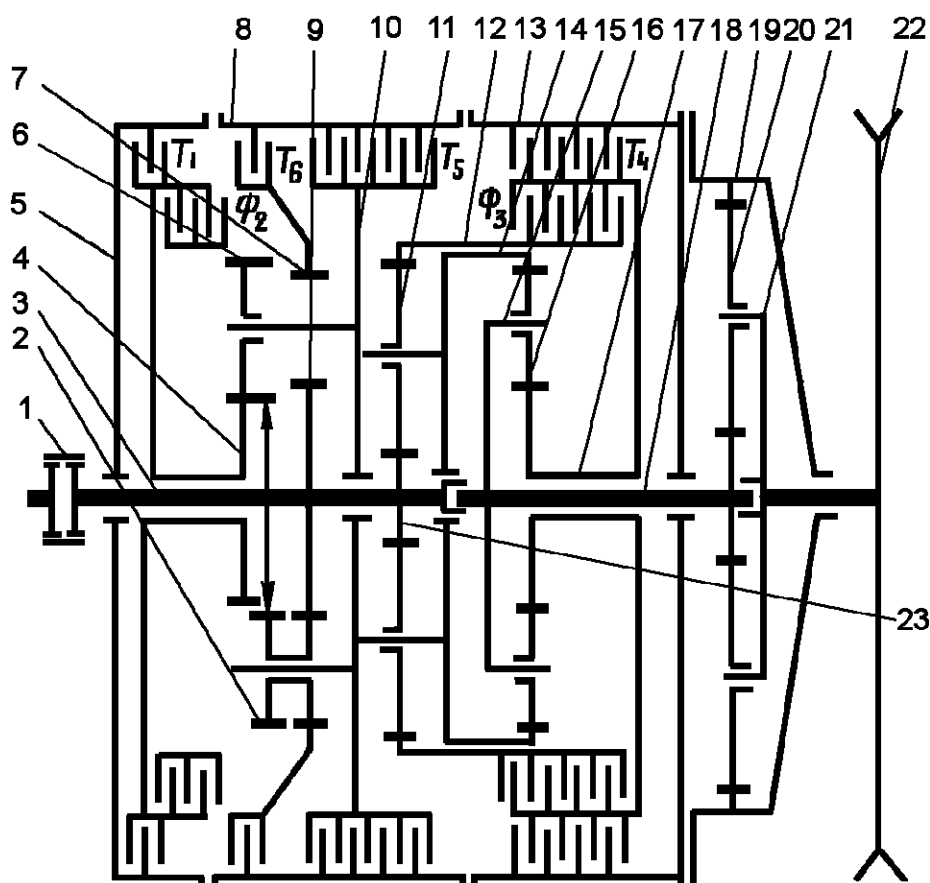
Кинематическая схема трансмиссии танка Т-72Б:
